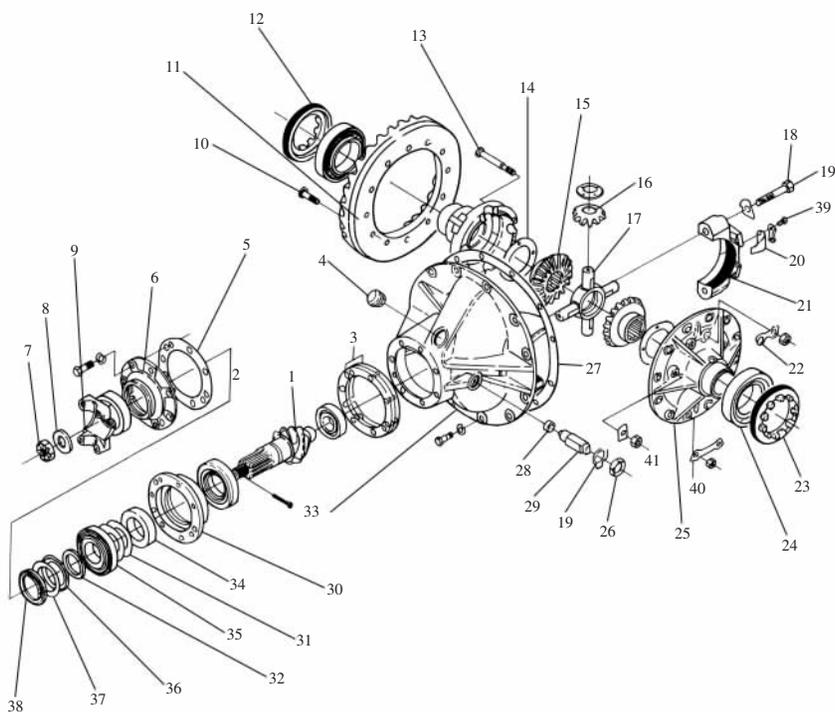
EQ1090 型汽车驱动桥减速器及差速器分解图
